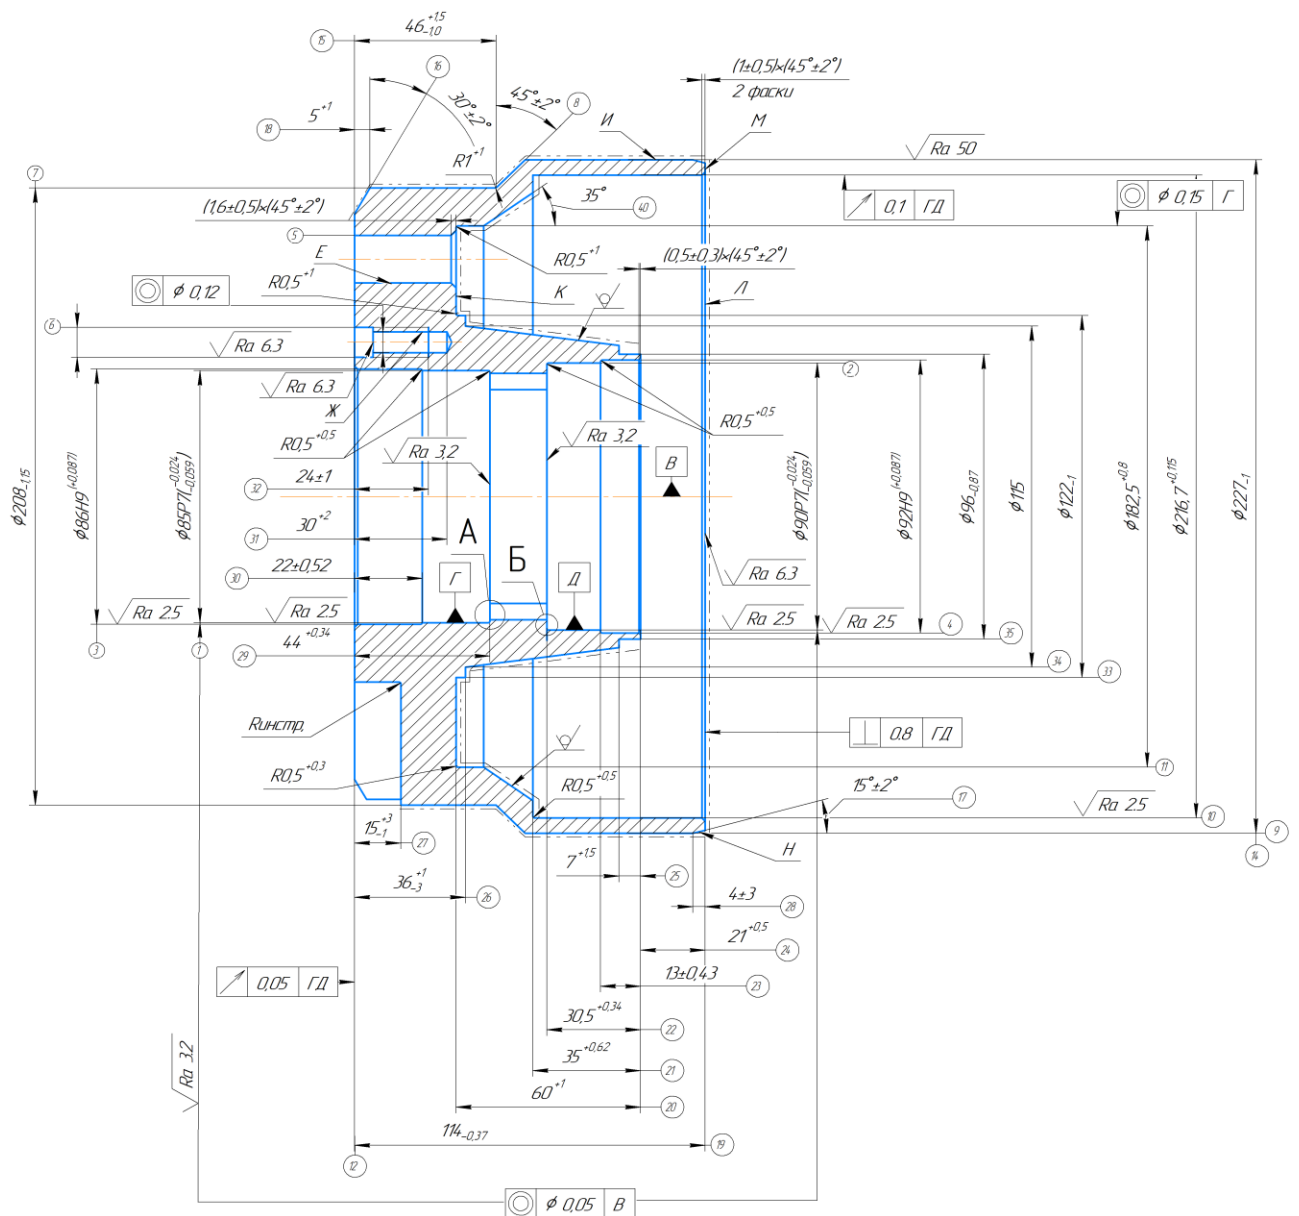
Вид А по чертежу. Нумерация поверхностей детали.
